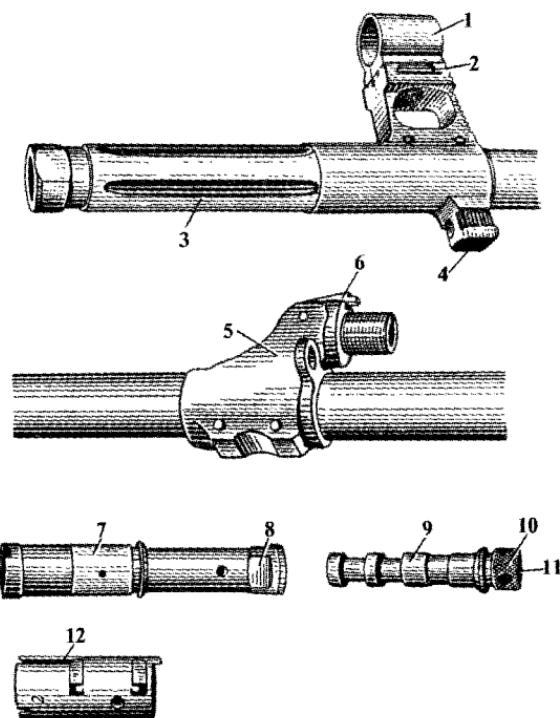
Мушка и газовая камора СВД-63: 1 — предохранитель мушки; 2 — паз для предохранителя мушки; 3 — пламегаситель; 4 — упор для штыка-попса; 5 — газовая камора; 6 — защелка газовой трубы; 7 — газовая трубка; 8 — четырехгранное утолщение для ключа пенала; 9 — газовый поршень; 10 — головка газового поршня, 11 — гнездо для толкателя; 12 — регулятор.
